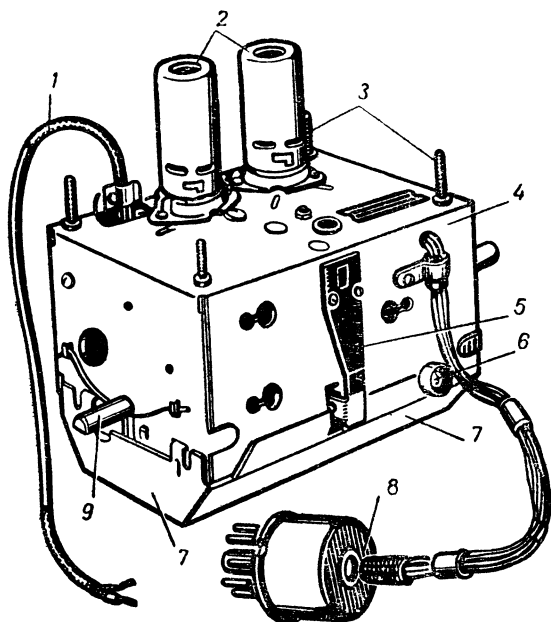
Общий вид блока ПТК: 1 — антенный кабель; 2 — экраны ламп; 3 — крепежные винты; 4 — корпус ПТК; 5 — пружина фиксатора; 6 — винт с чашечкой для пломбы; 7 — нижняя крышка; 8 — фишка включения ПТК в телевизор; 9 — ось барабана переключателя каналов
